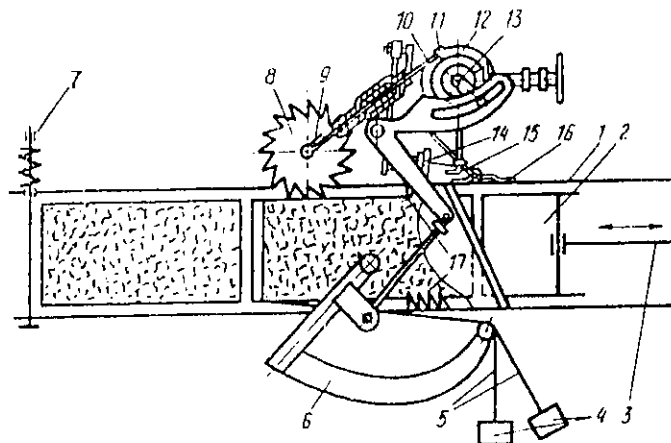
Прессовальная камера с вязальным аппаратом: 1-прессовальная камера; 2-поршень; 3-шатун; 4-кассеты; 5-проволока или шпагат; 6-игла; 7-регулятор плотности; 8-мерительное колесо; 9-палец; 10-рычаг включения; 11-собачка; 12-муфта; 13-вал; 14-нож-зажим; 15-крючок-вязатель; 16-направляющая проволоки; 17-пазообразователь.
